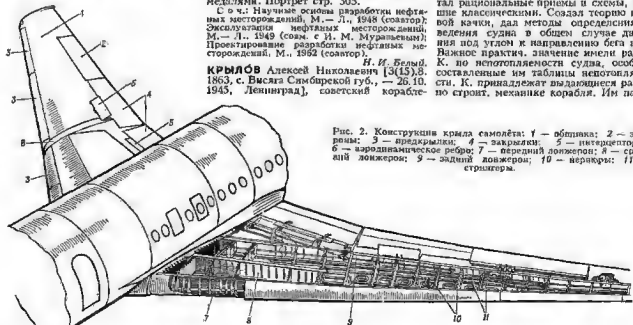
Конструкция крыла самолета: 1 — обшивка; 2 — элероны; 3 — предкрылки; 4 — закрылки; 5 — интердуги; 6 — аэродинамическое ребро; 7 — передний доверток; 8 — средний доверток; 9 — задний доверток; 10 — нервюры; 11 — стрингеры.
